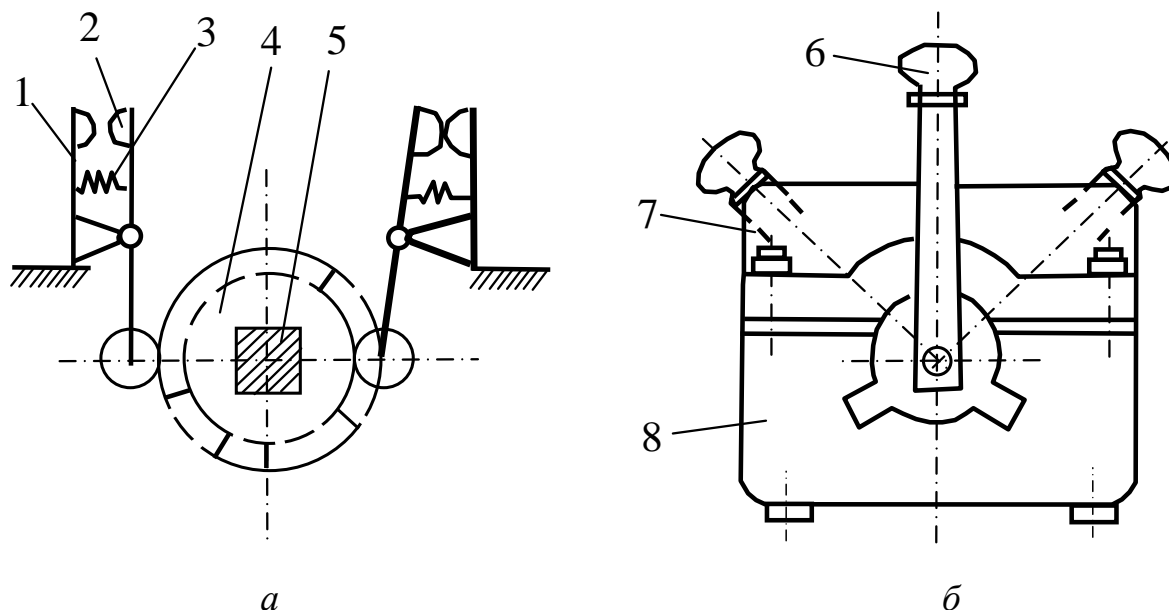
Кулачковый контроллер ККТ-61:
